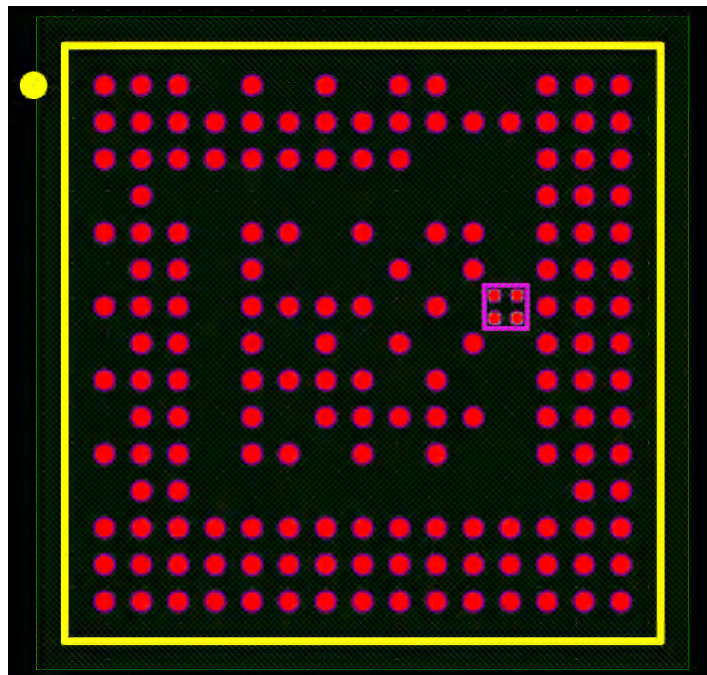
PCB 编辑器中 IWR6843 和 TMP114 呈现的尺寸
